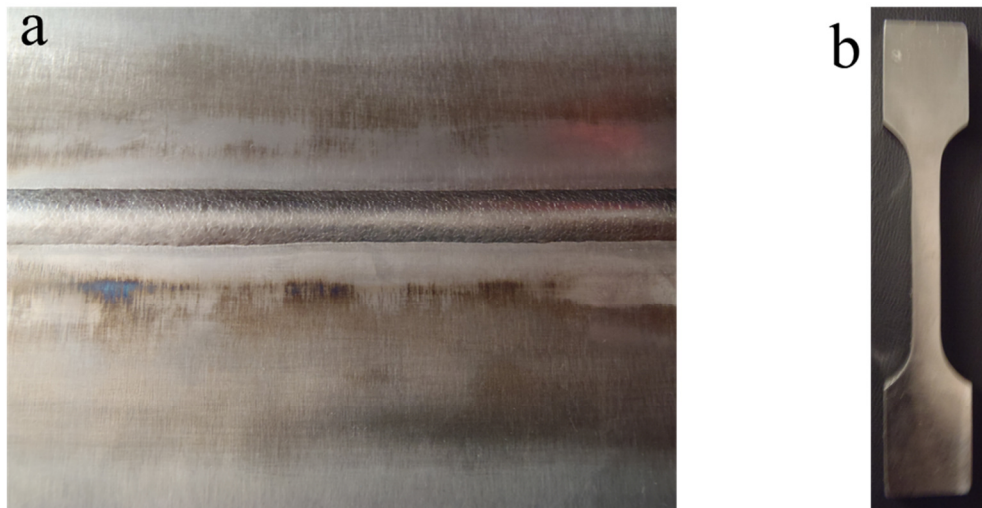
A) Unión Soldada GTAW, B) especímenes utilizados.
